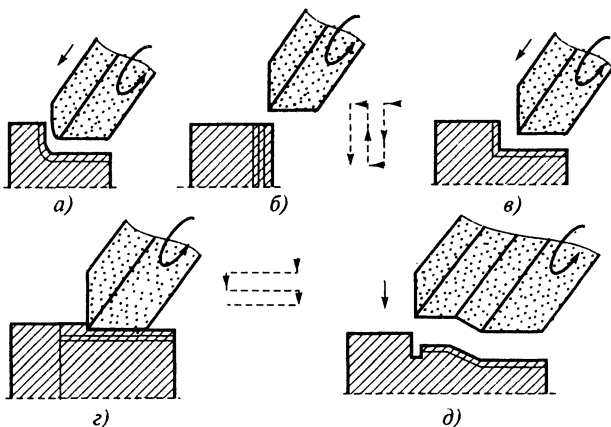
Схема обработки на торцекрылошлифовальном станке с ЧПУ
